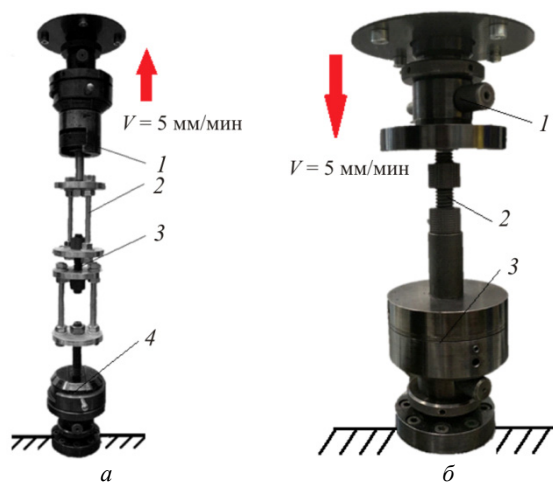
Фотографии оснасток для испытания в сборе: а – на разрыв (1 – активный захват, 2 – оснастка на разрыв, 3 – резьбовой образец на разрыв, 4 – зафиксированный захват); б – на сжатие (1 – активный стол, 2 – резьбовой образец, 3 – зафиксированный стол)
